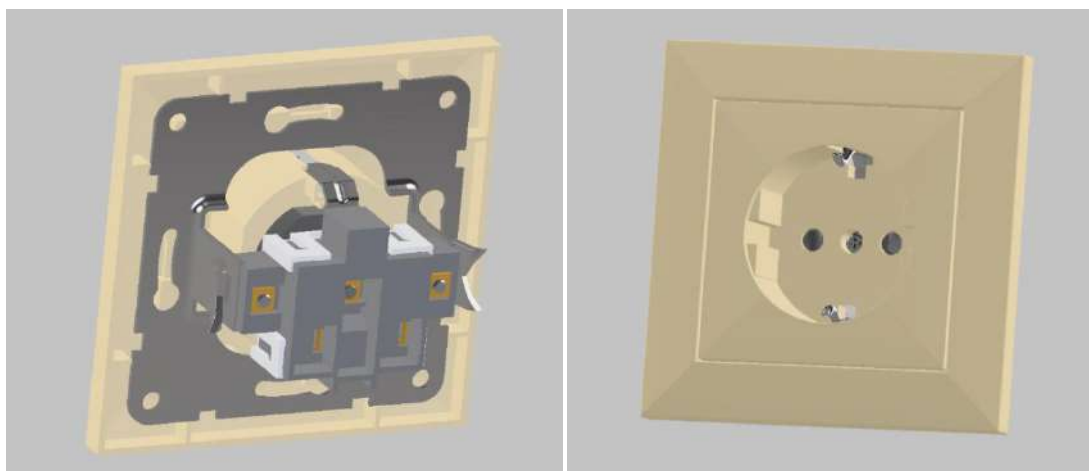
3D-модель розетки LK60 с з/к и с защитными шторками
